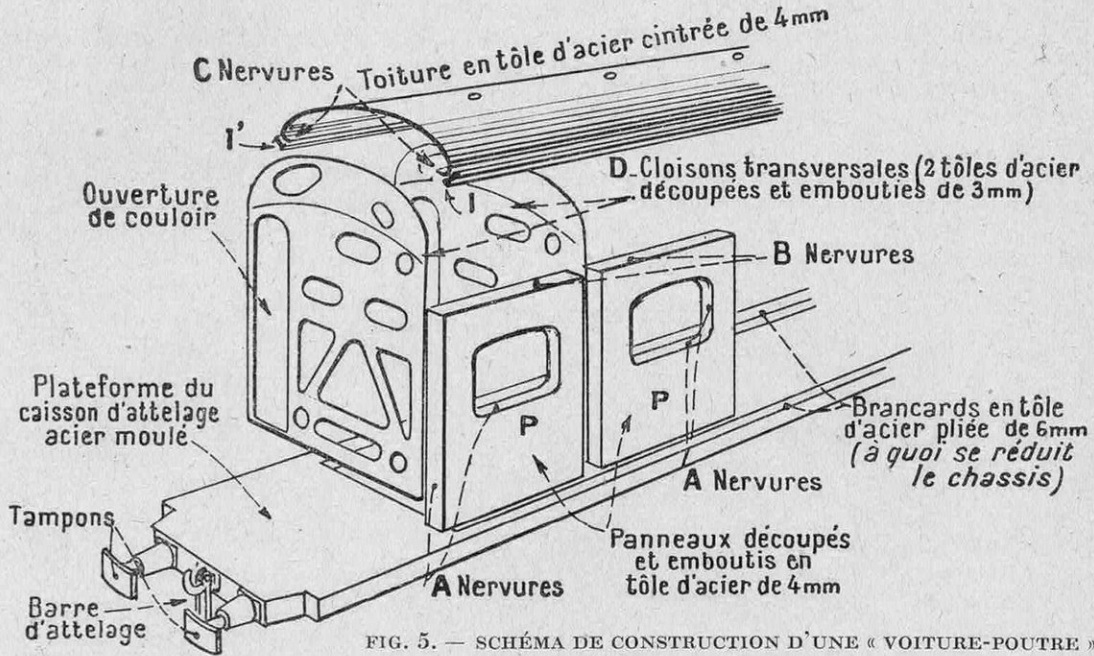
SCHÉMA DE CONSTRUCTION D'UNE « VOITURE-POUTRE »
